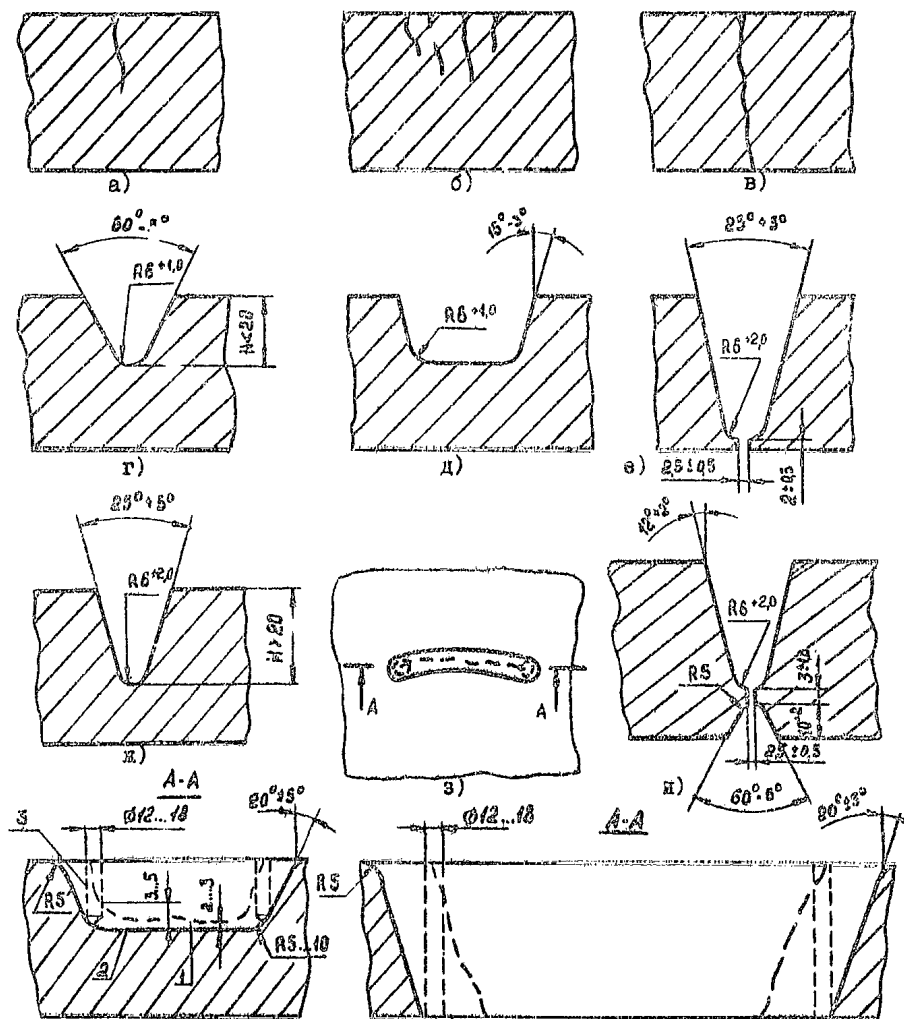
Разделка сквозных и несквозных трещин под дуговую сварку.
